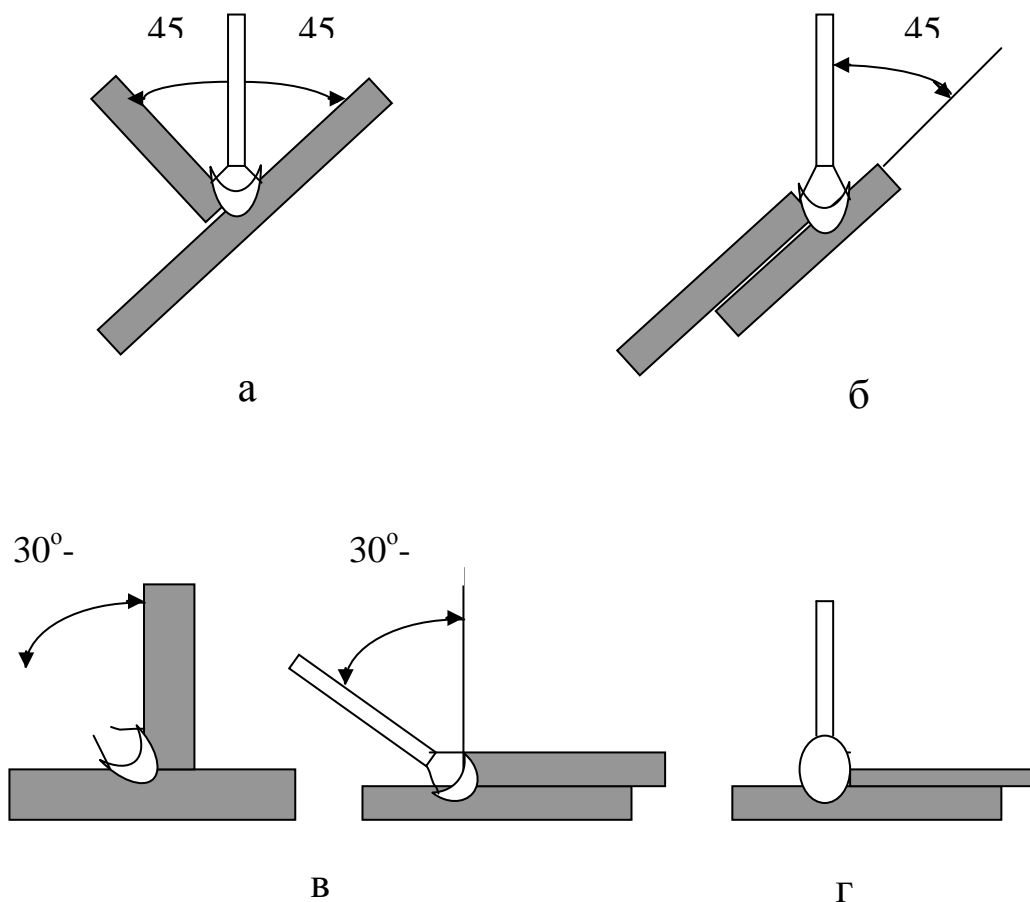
Способи зварювання кутових швів: а, б – в симетричну лодочку; в – зварювання в кут; г – зварювання з оплавленням кромок
